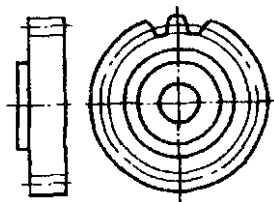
Изображение профиля зуба зубчатого колеса
